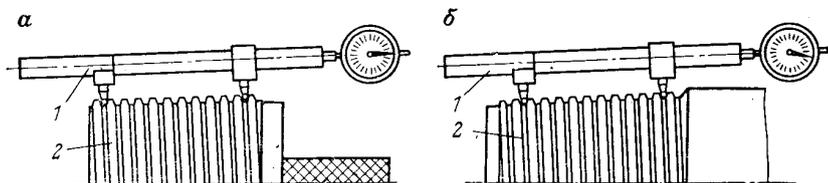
Схема проверки отклонения шага резьбы шагомером ШИ трапецидальных резьб ТТ труб:
